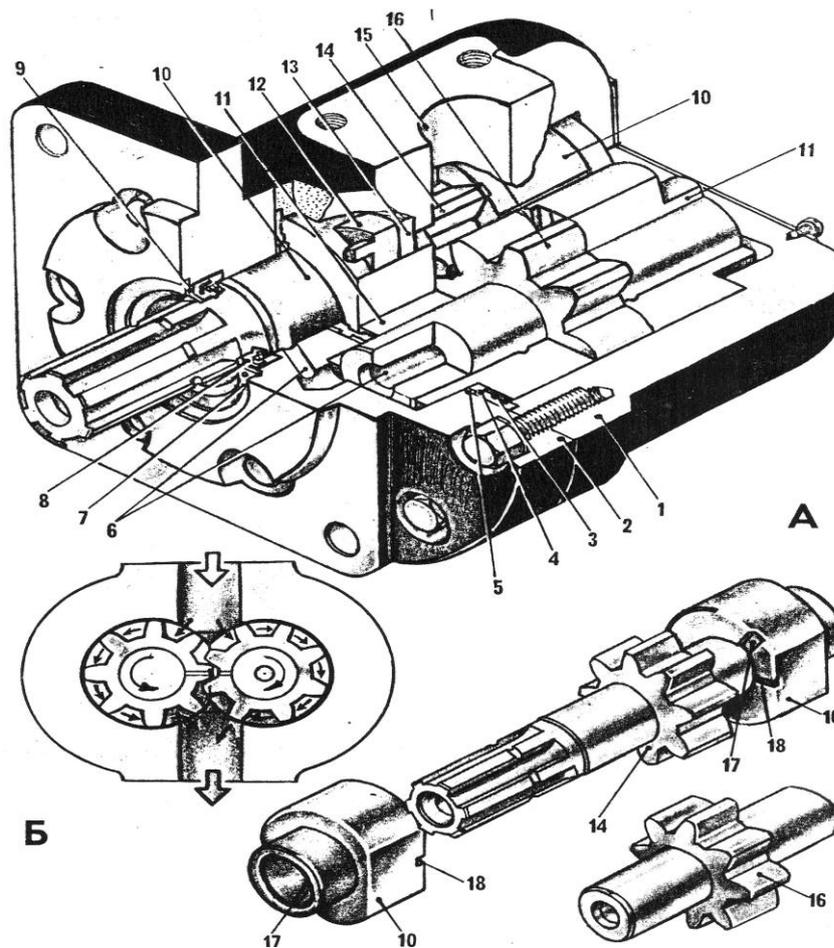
Шестеренный насос: А - устройство; Б - схема работы; 1 - корпус; 2 - крышка; 3 - полость для масла; 4 - резиновая манжета; 5 - кольцо; 6 - отверстие для отвода масла; 7 - стопорное кольцо; 8 - сальник; 9 - опорное кольцо; 10 - опорная втулка ведущей шестерни; 11 - опорная втулка ведомой шестерни; 12 - резиновая втулка; 13 - вкладыш; 14 - ведущая шестерня; 15 - впускное отверстие; 16 - ведомая шестерня; 17 - канавки для смазки оси шестерни; 18 - разгрузочные канавки
